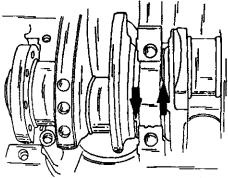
Здесь вставляются распорные шайбы для регулировки осевого люфта коленчатого вала.
